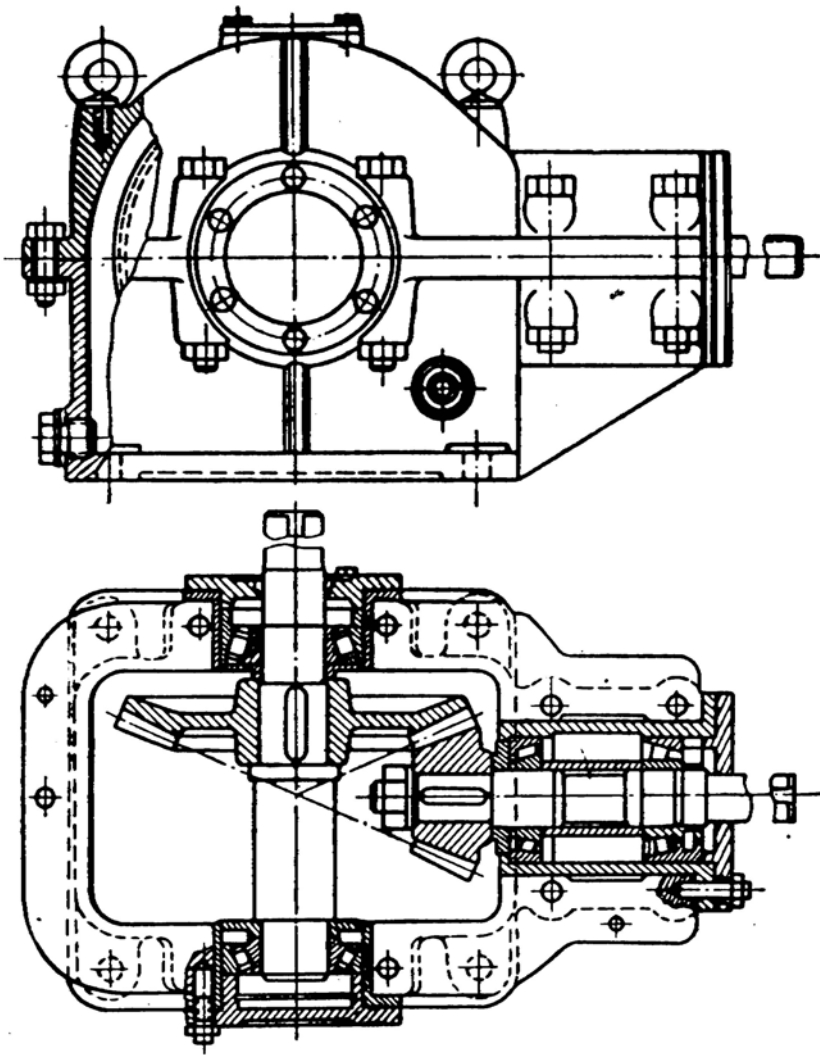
22 Одноступенчатый редуктор с коническими зубчатыми колесами
